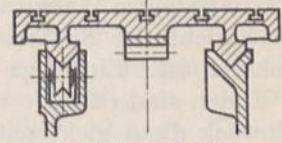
Schlittenführung an Werkzeugmaschinen.
